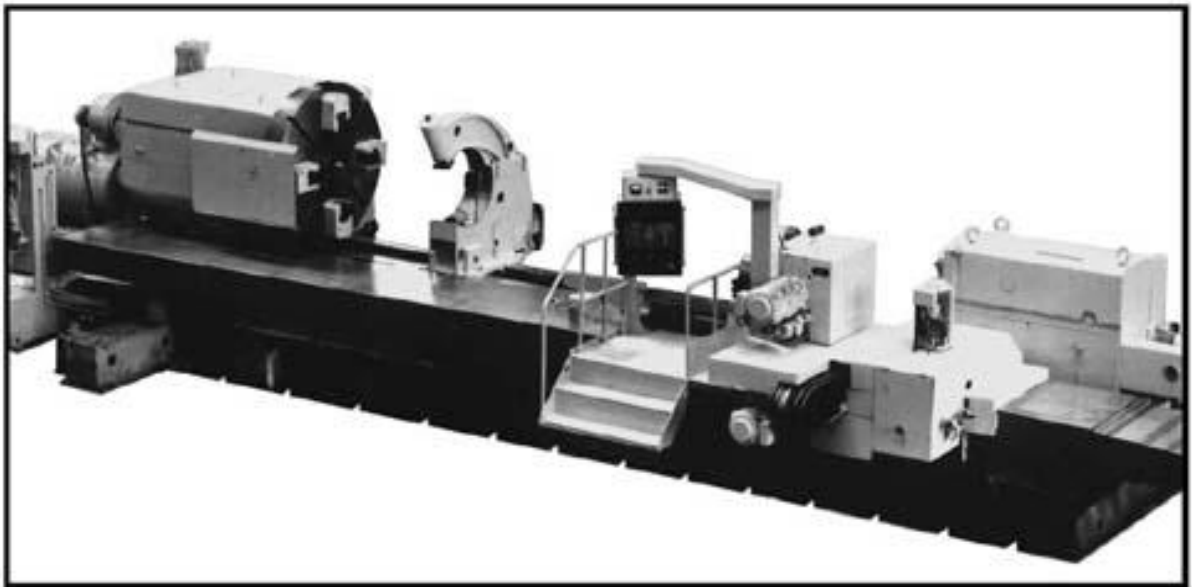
Загальний вид токарного верстата мод. 1K665Ф3
